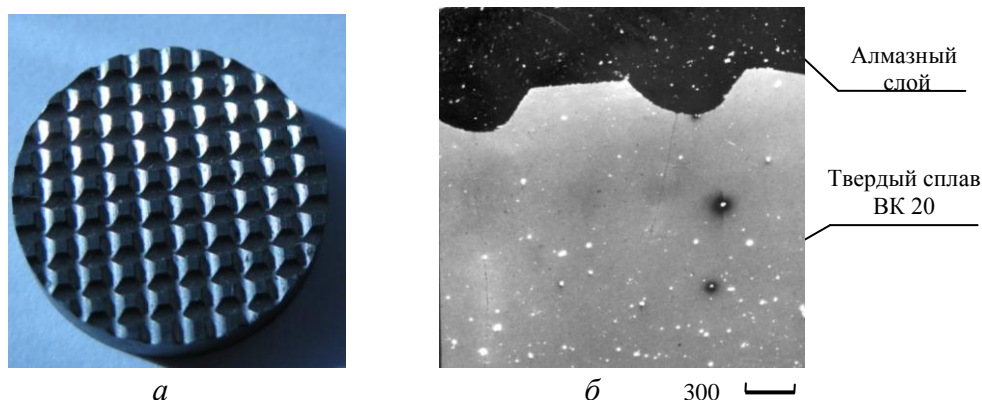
Подложка с шахматными насечками: а – общий вид; б – профиль фигурного паза
